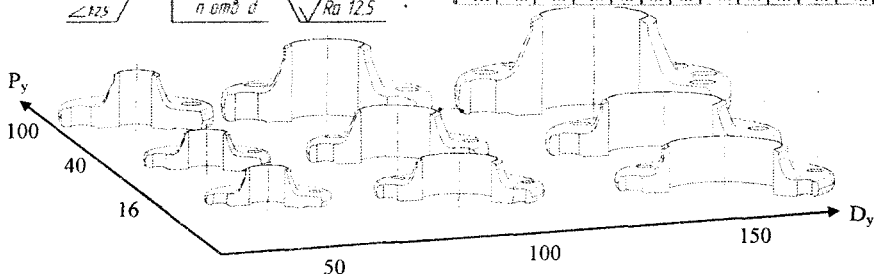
Типоразмеры стандартных фланцев воротниковых
